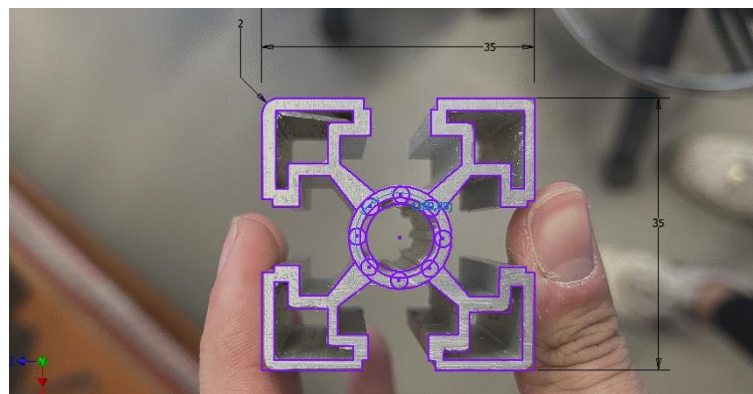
Planta del perfil con boceto en Autodesk Inventor
